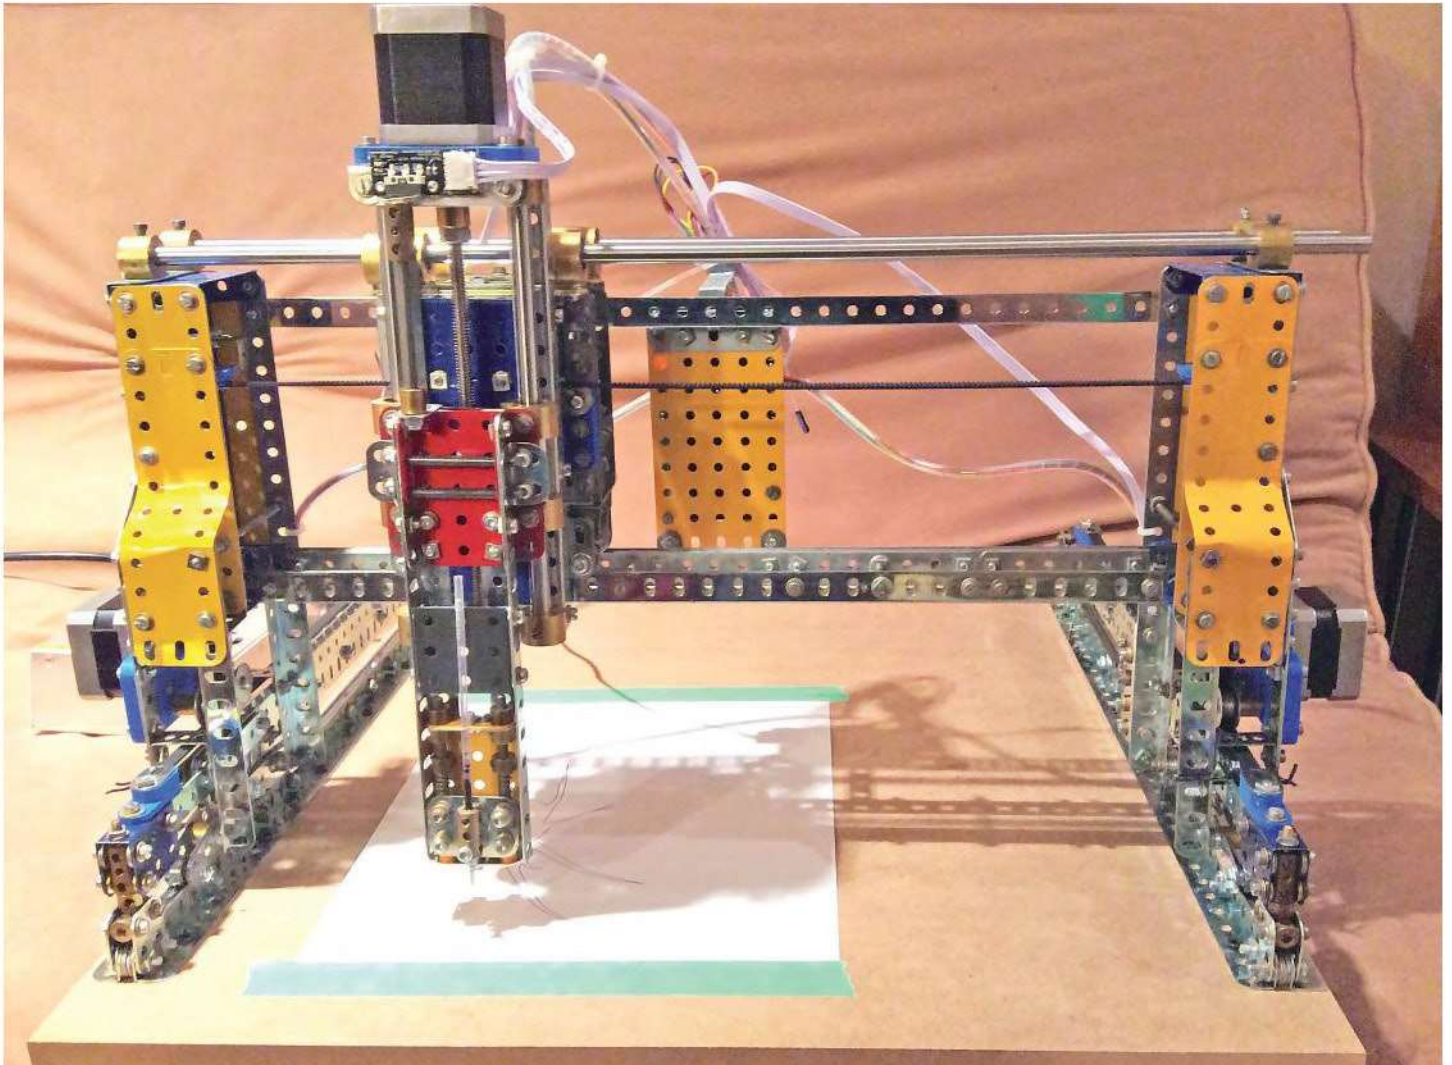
La quatrième génération de CNC, une fraiseuse pour machiner des matériaux mous, comme le plastique ou le bois
